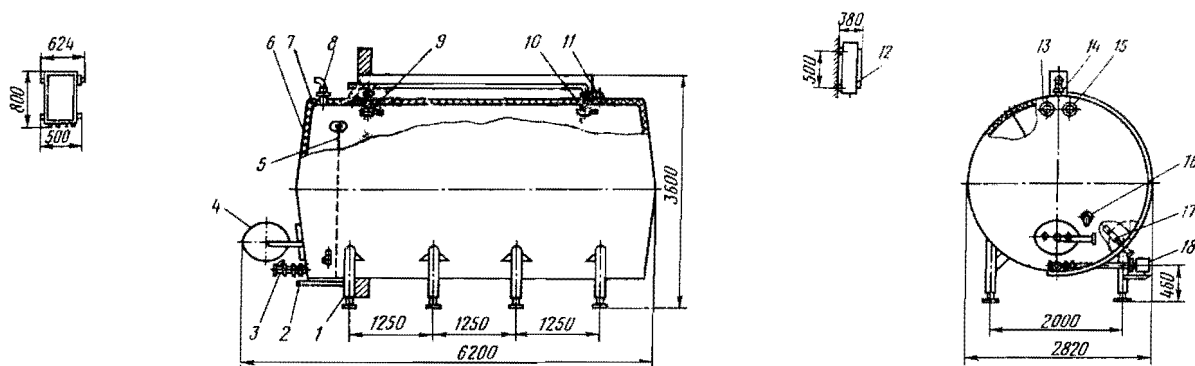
Общий вид резервуара марки Г6-ОМГ-25:
